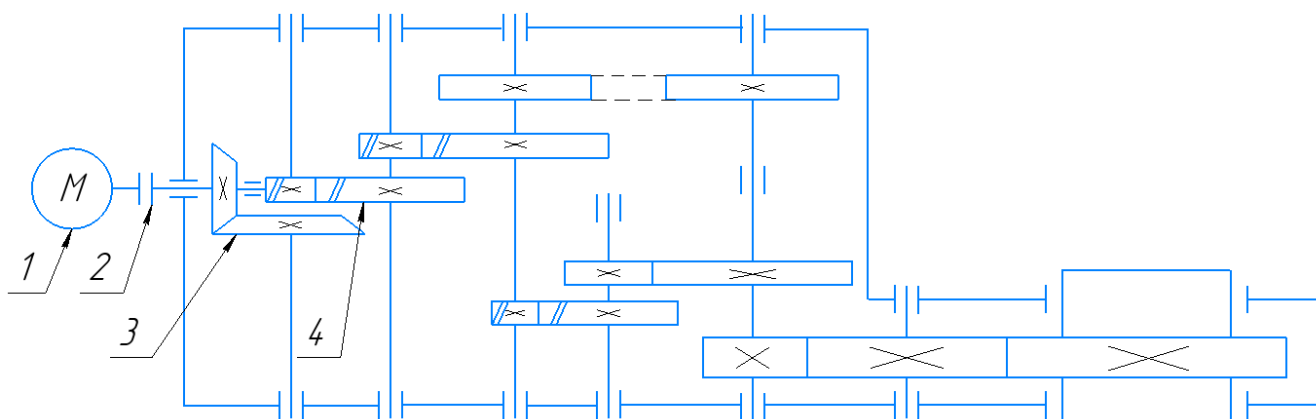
Кинематическая схема червячного цилиндрического редуктор (supertronic 1250)
